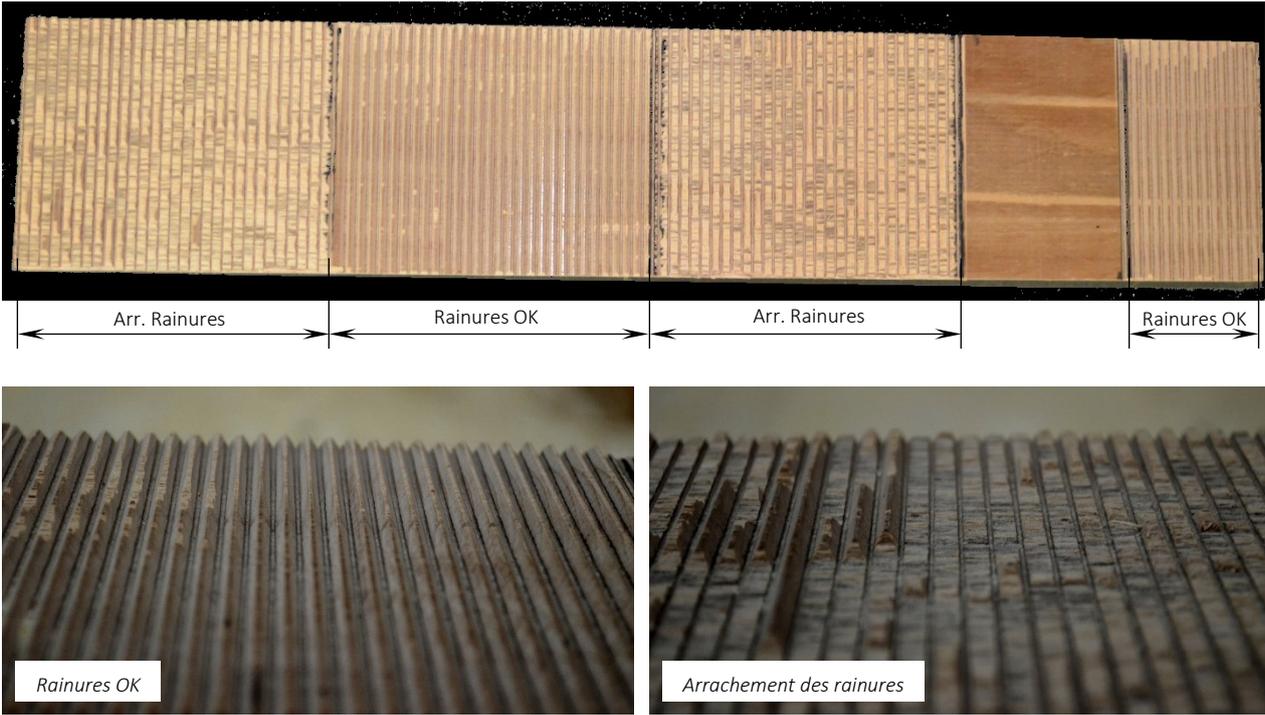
Essais de rainurages transversaux sur LVL Q non raboté
